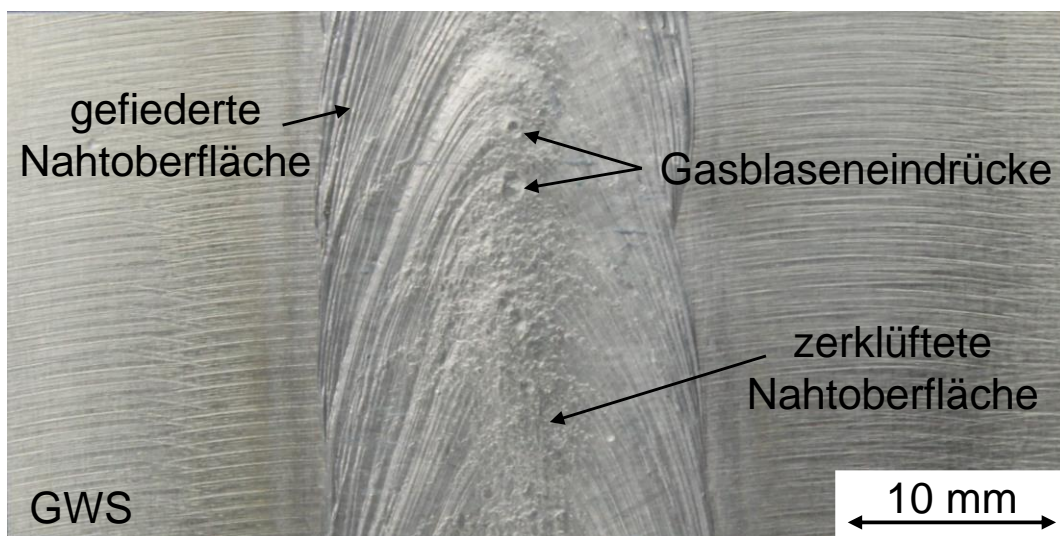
Schweißraupe auf Grundwerkstoff mit Kennzeichnung von Gasblaseneindrücken, gefiederter Nahtoberfläche und zerklüfteter Nahtoberfläche
